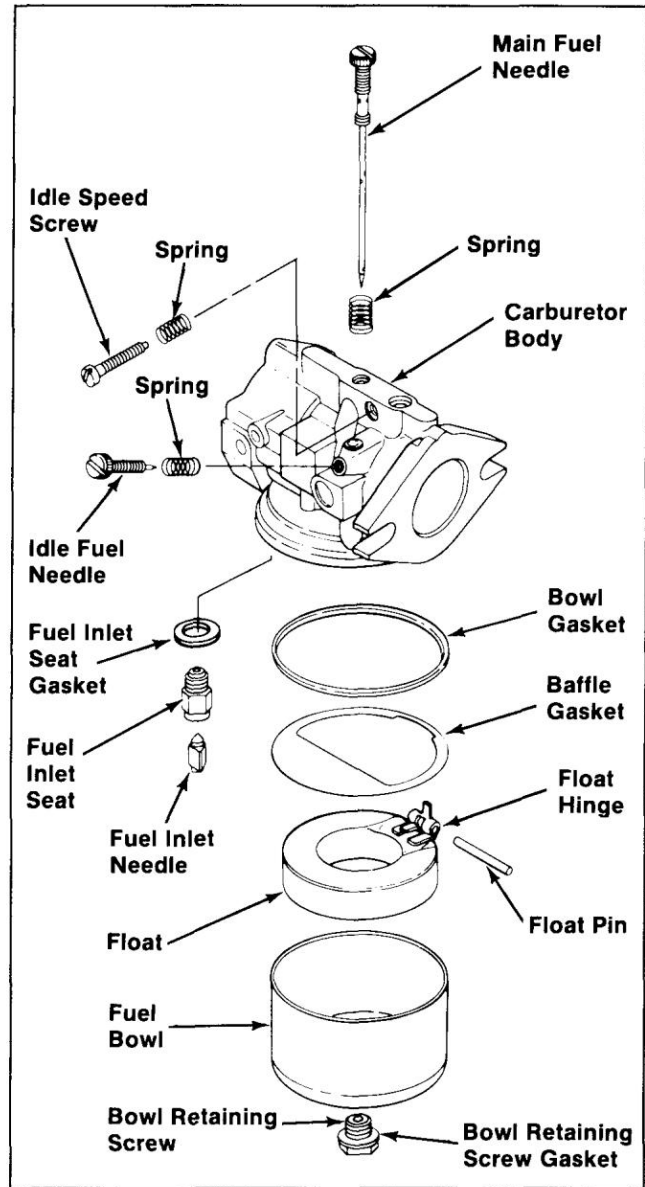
Carburateur à jet réglable construit par Kohler - Vue éclatée.
